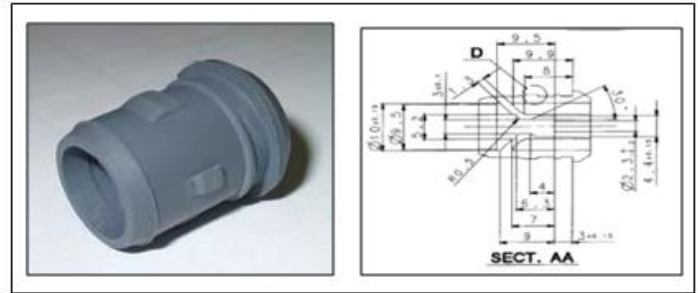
Dibujo de la pieza socket. Fuente: Los autores, 2015.
